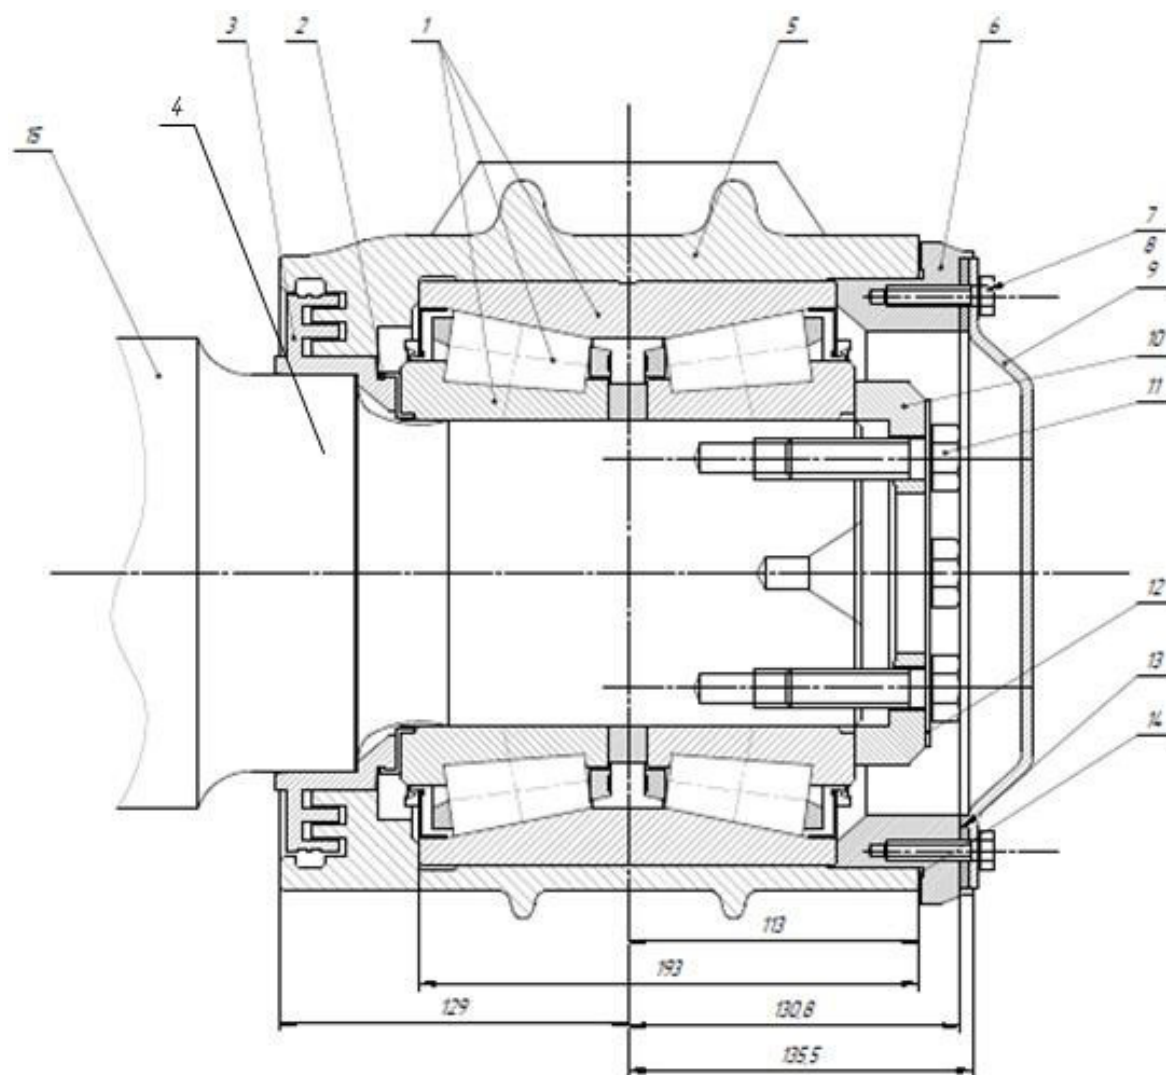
Буксовый узел грузового вагона с коническими роликовыми подшипниками кассетного типа:
